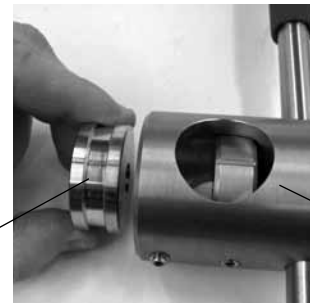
Lösen der Sicherungsschrauben für die Hülse des Gewindeschneidwerkzeugs (die zweite Schraube befindet sich auf der anderen Seite des Gehäuses)
